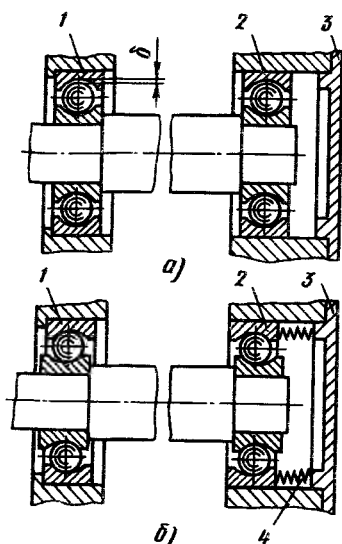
Положение колец и шариков без предварительного натяга (а) и с предварительным натягом (б)
